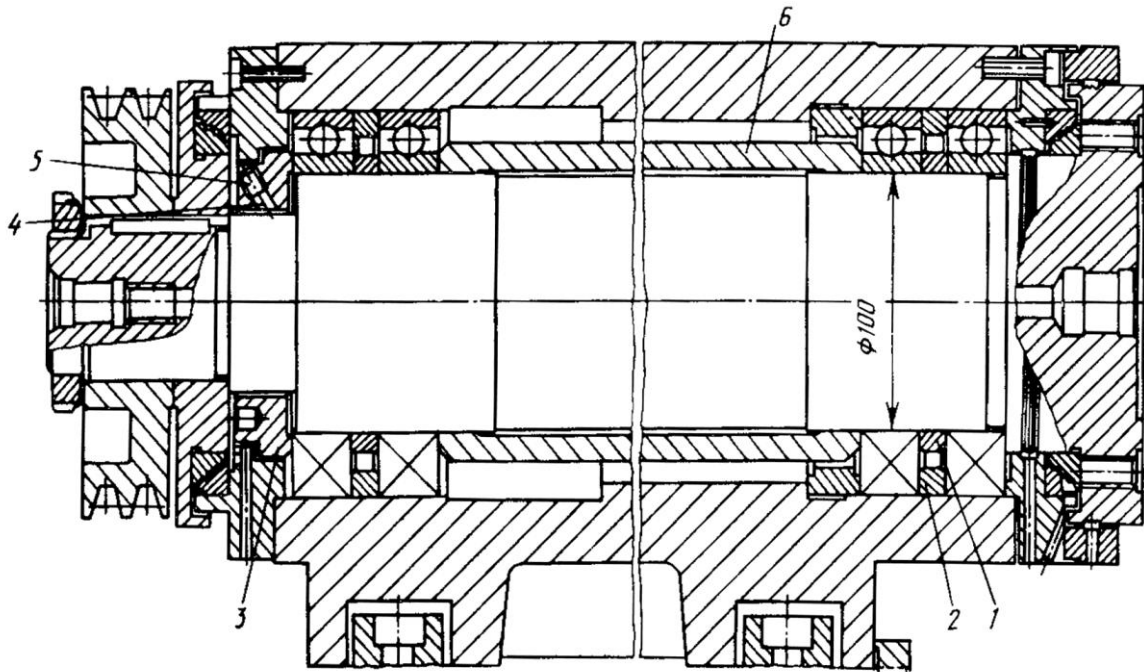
Шпиндельний вузол розточувальної головки
